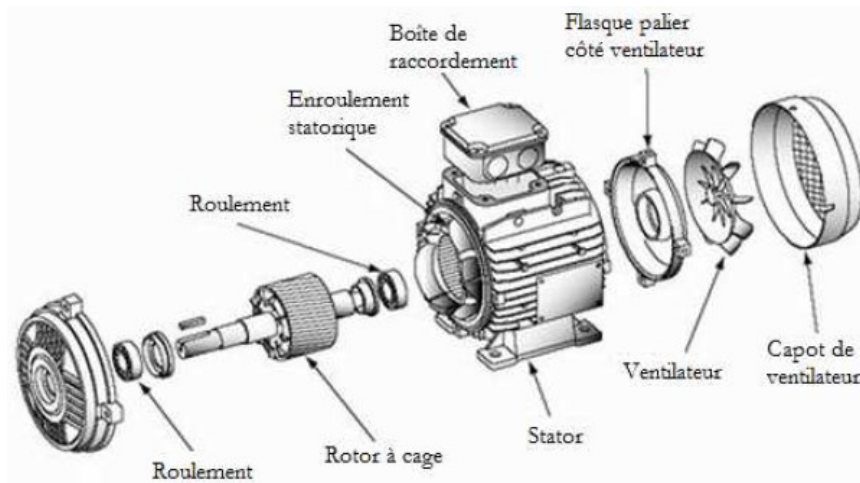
Vue éclatée d'une machine asynchrone à cage fermée auto-ventilée [5].
